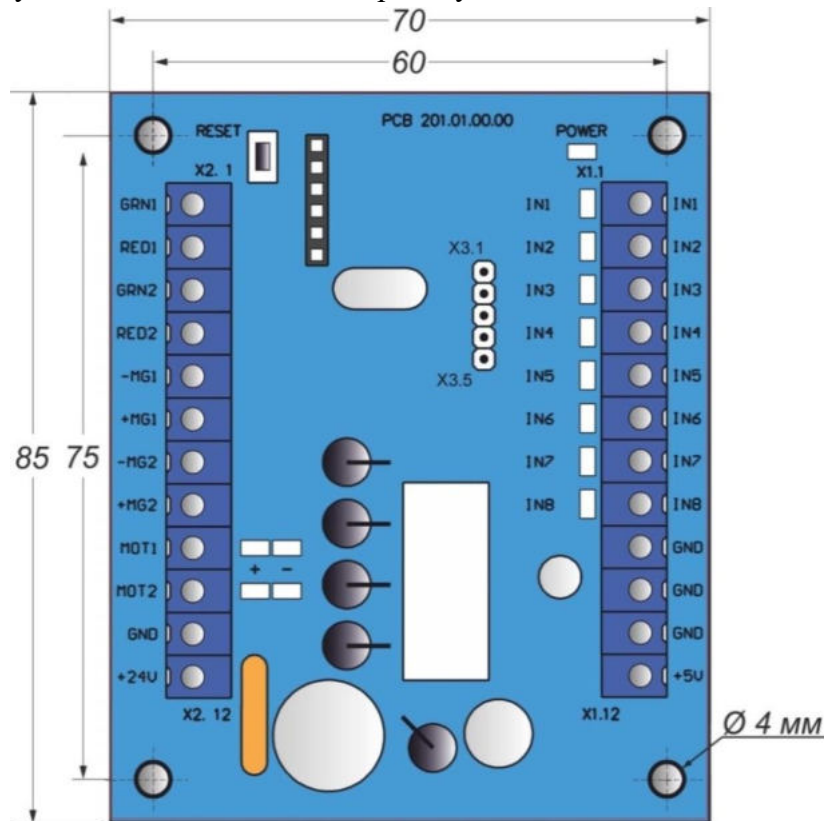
Зовнішній вигляд, габаритні та приєднувальні розміри контролера PCB.201.01.00.00
